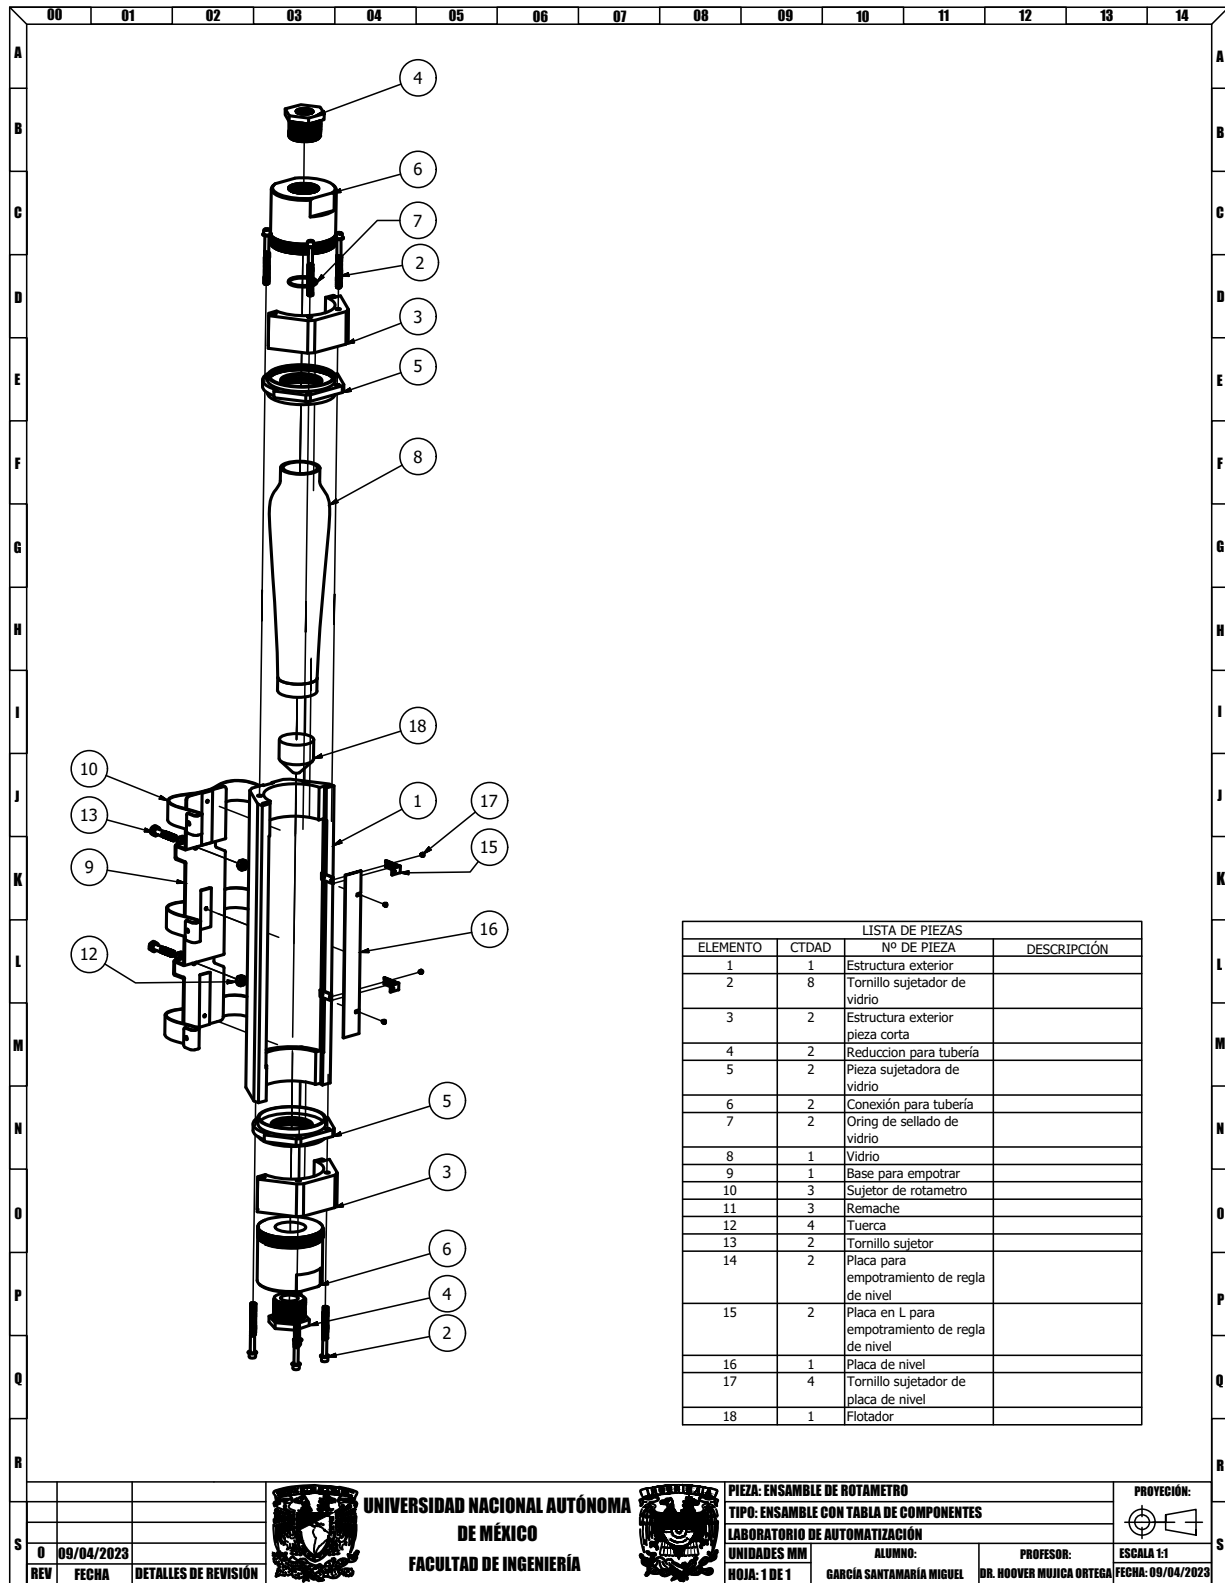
Ensamble explosionado y tabla de componentes de rotámetro
